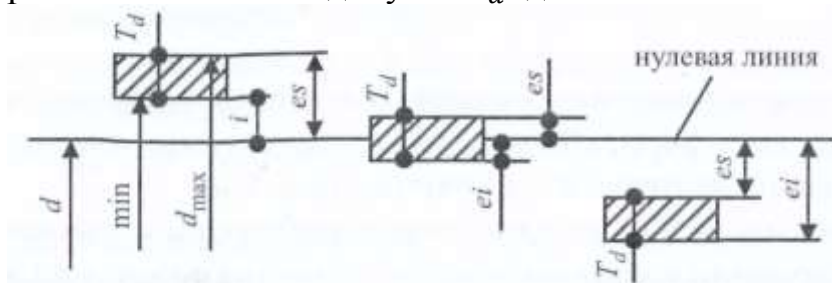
Варианты расположения поля допуска вала относительно нулевой линии.
